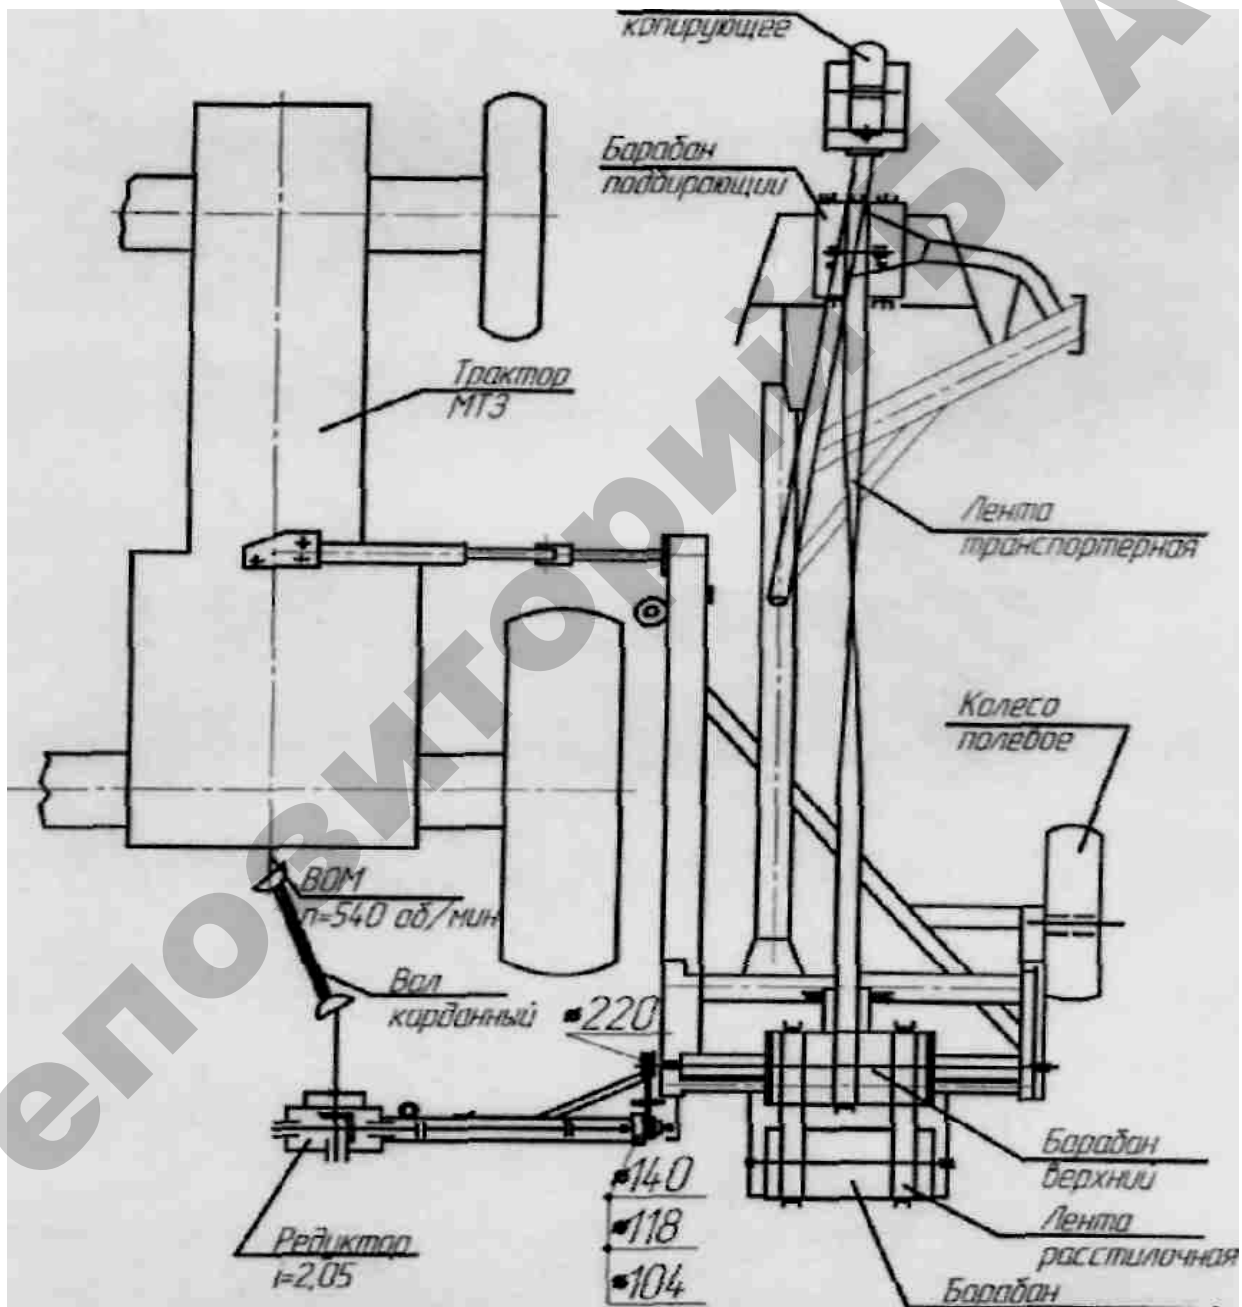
Кинематическая схема оборачивателя ОЛ-1М
